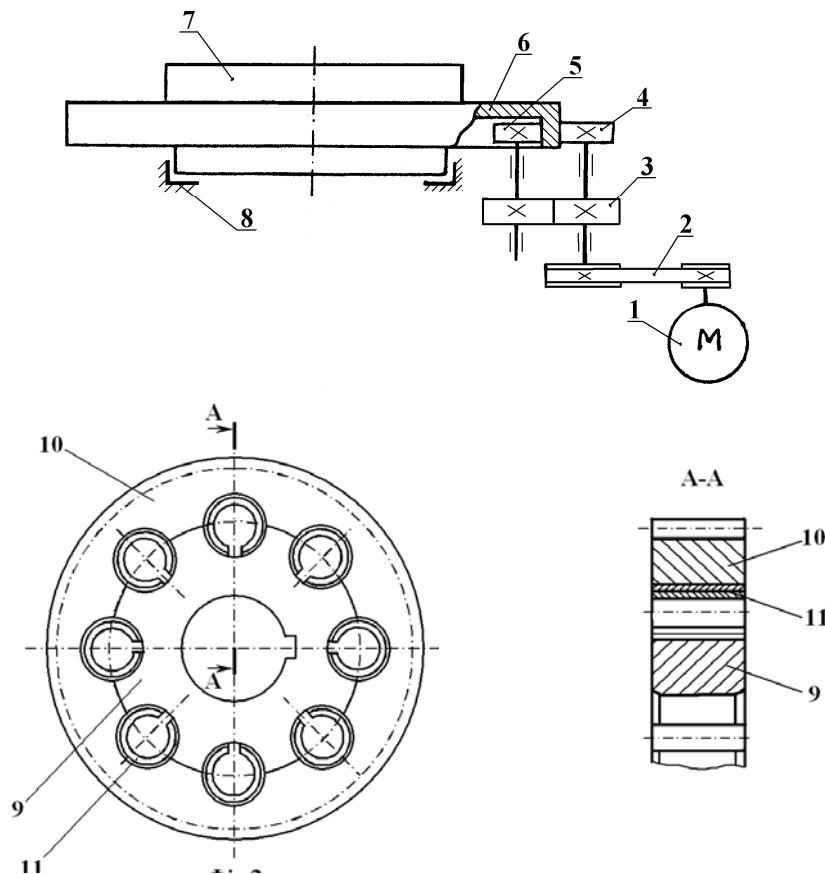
Схема привода круглов'язальної машини з шестернями з гільзовими пружинами
